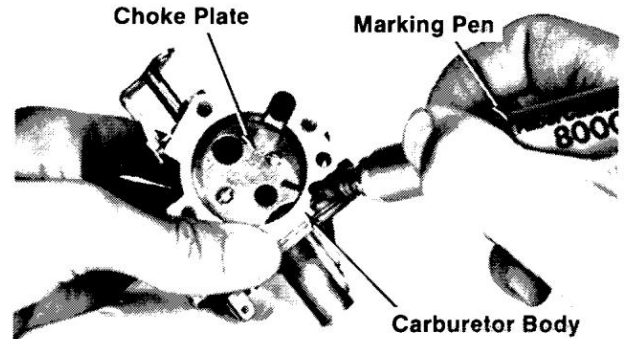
Marquage de la plaque de starter et du corps du carburateur.
